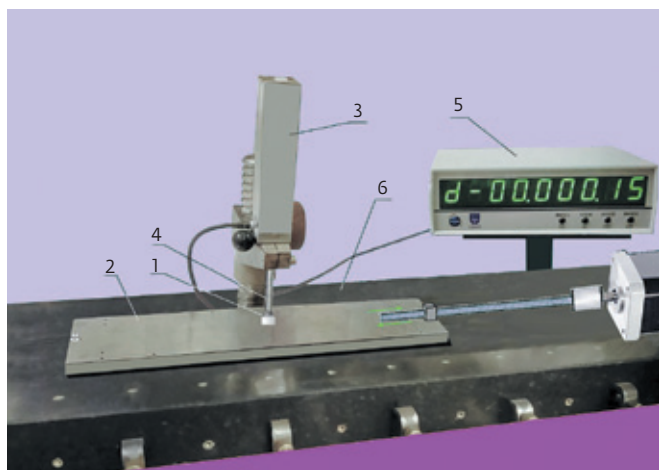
1 – подшипник скольжения, 2 – исследуемая металлическая плита, 3 – длиномер голографический ДГ-30, 4 – шток длиномера, 5 – блок управления длиномера, 6 – поверхность габродиабазовой опорной плиты
